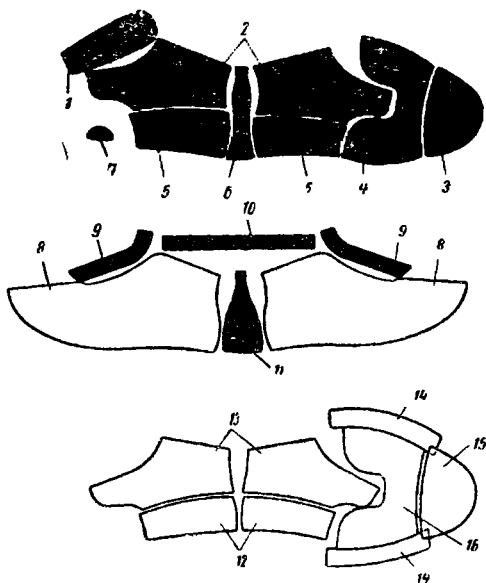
Детали заготовки ботинка с отрезными деталями:
